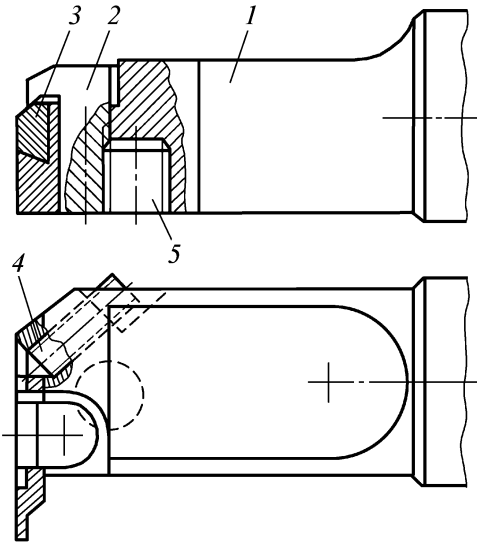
Расточный резец с механическим креплением канавочной твердосплавной пластины:
